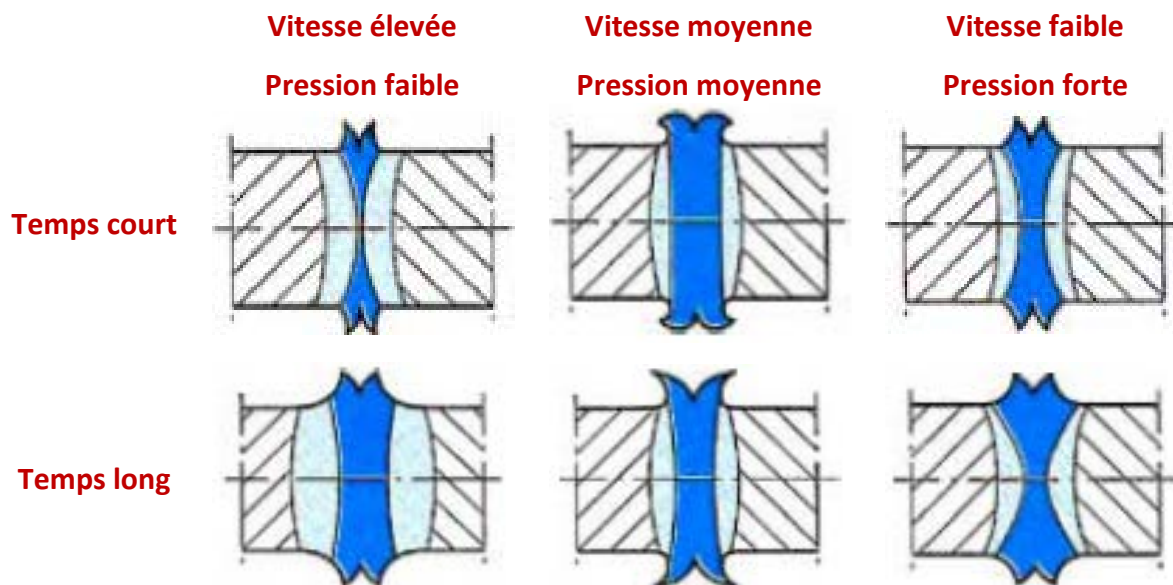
Effet des paramètres de soudage sur la forme des joints soudés par RFW [14]
